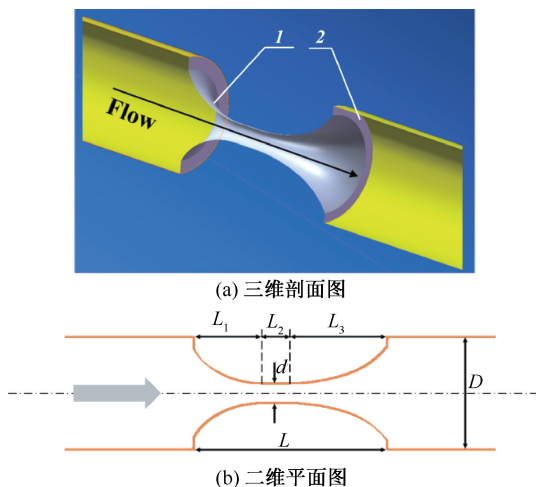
第 1 代激波雾化喷嘴的三维剖面图和二维平面图
